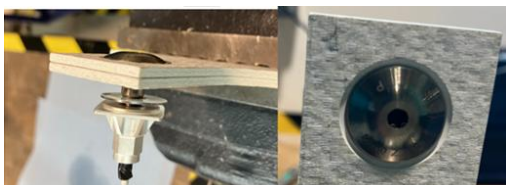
Montage d'un assemblage boulonné de pièces en CMC oxyde
